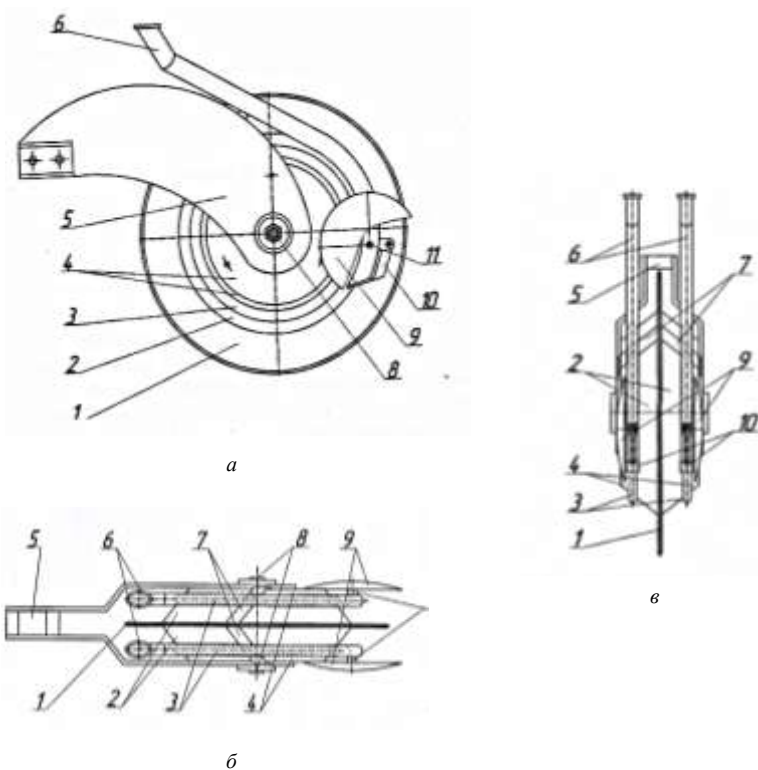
Комбинированный однодисковый сошник с двухсторонними ребрами и дисковыми загортачами с нулевым углом атаки дисков для узкорядного посева: *а* – вид сбоку; *б* – вид сверху; *в* – вид сзади: 1 – плоский диск; 2 – внутренняя реборда; 3 – бороздкообразователи; 4 – наружная реборда; 5 – корпус; 6 – семянаправители; 7 – чистики; 8, 11 – оси; 9 – сферический диск; 10 – клапан
